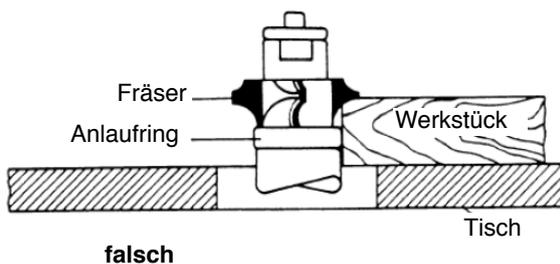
Fräsen mit Anlaufring unter dem Fräser
